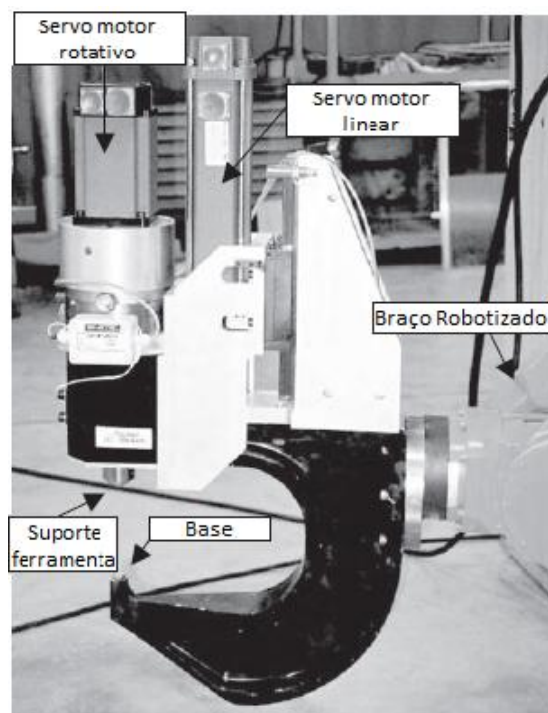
Dispositivo de soldagem por fricção e mistura mecânica - Tipo C.
